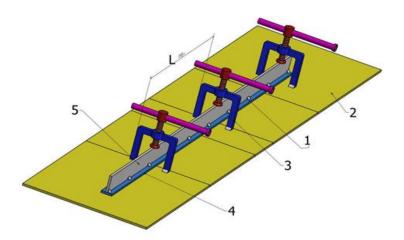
Сборка узла тавра с применением прижимов с П-образными приварными скобами:
